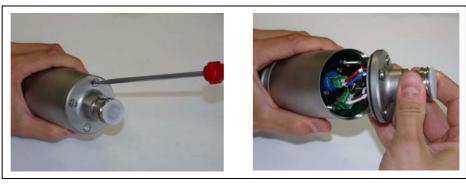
Quitar las tuercas cilíndricas y sacar la placa trasera
